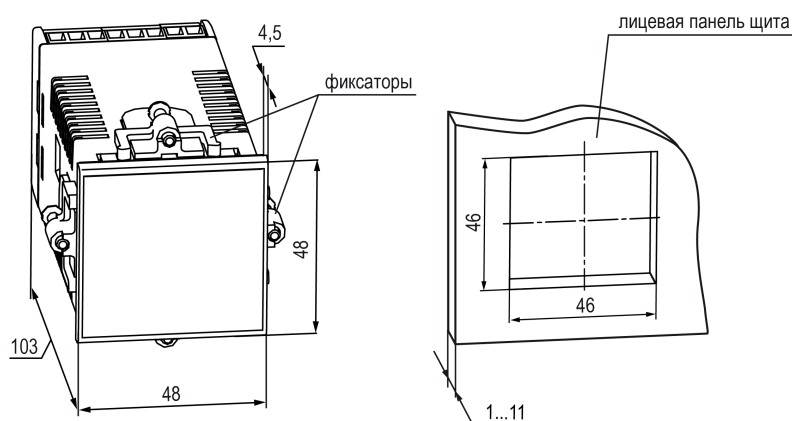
Габаритные размеры корпуса Щ5 и монтажного отверстия в щите
